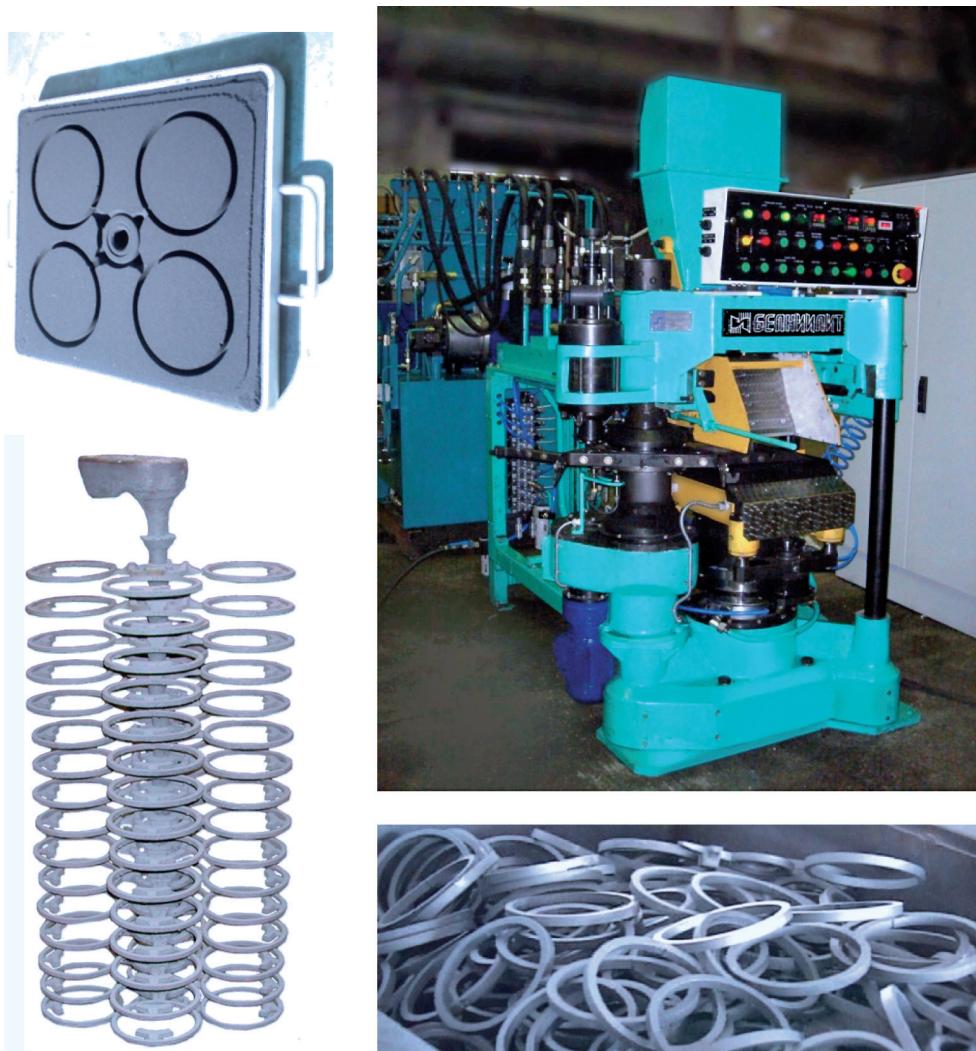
Машина вертикально-стопочной формовки мод. 4812, форма и отливки
